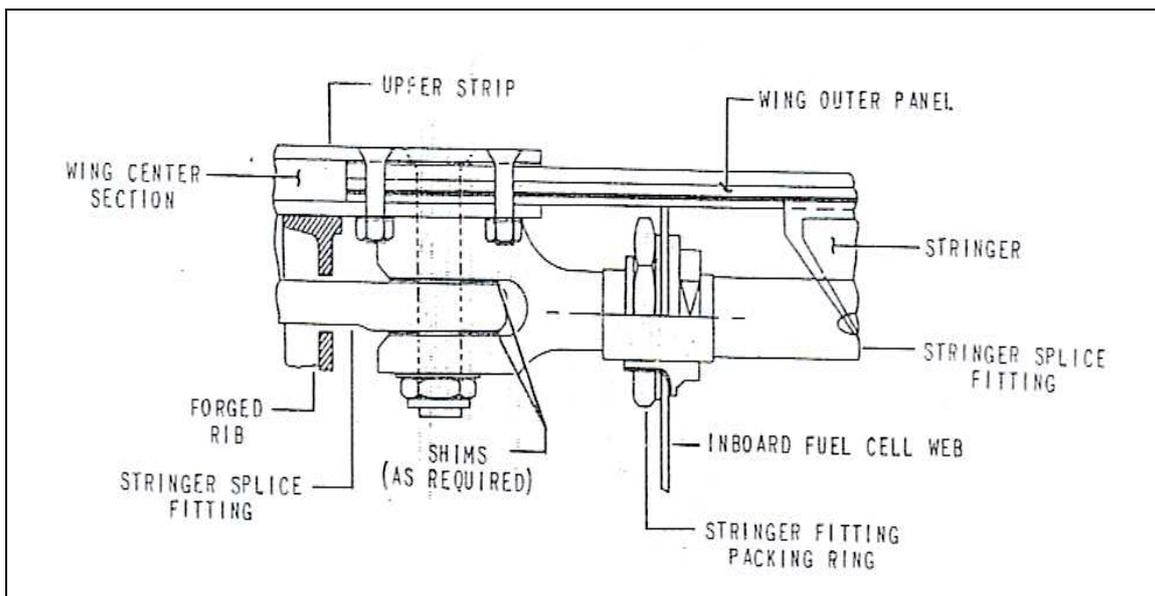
Wing Center Section Upper Stringer Fittings Installation
